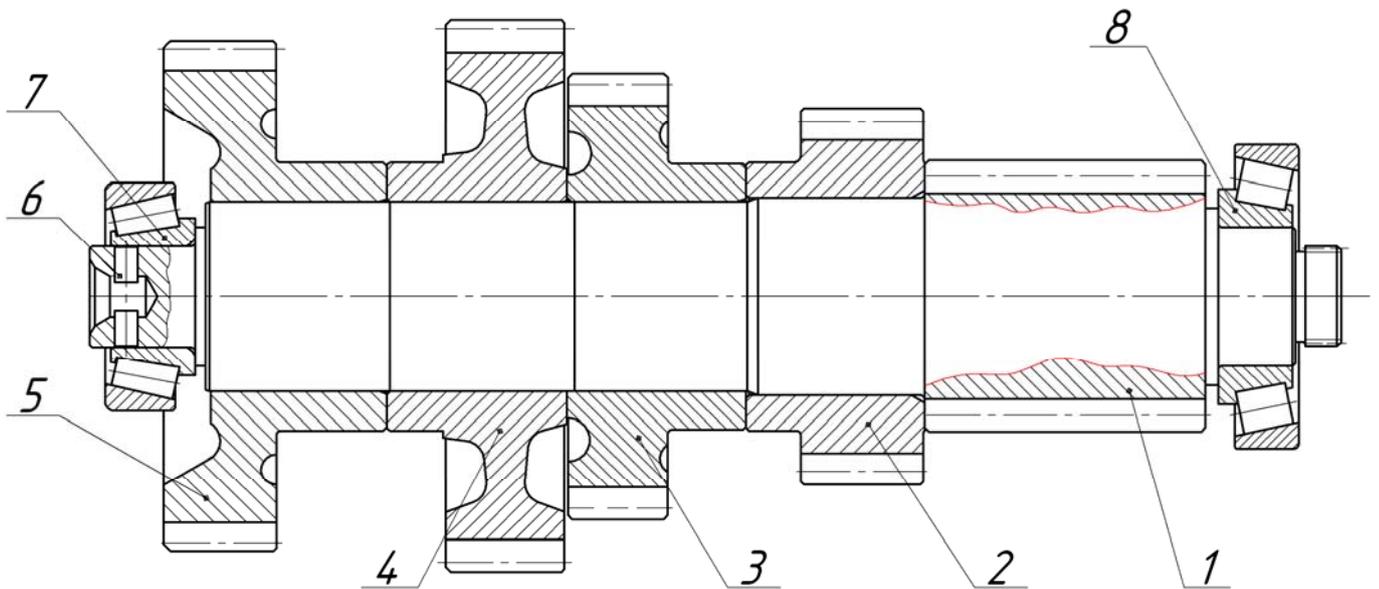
Вал первичный в сборе с трубкой и роликовым подшипником 6-7517АК (без наружной обоймы), дет. 239-1701025-10, + с внутренней обоймой переднего роликового подшипника вторичного вала 6-7608А1К и регулировочной прокладкой
